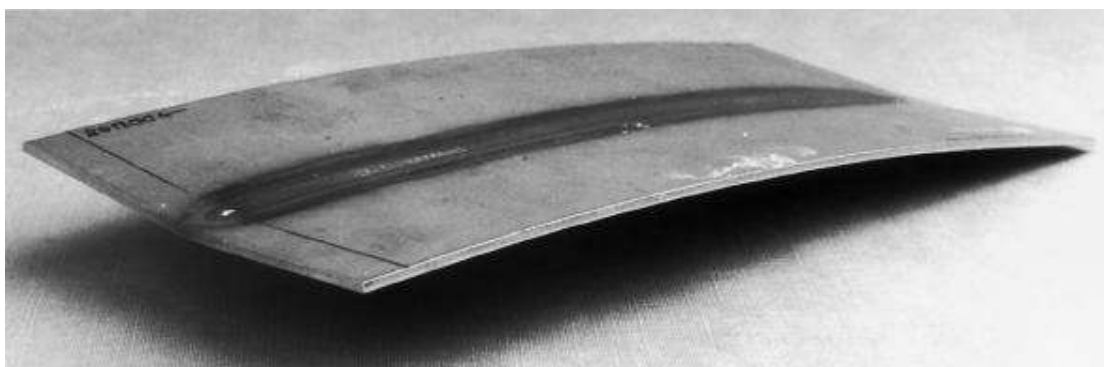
PLACA DE INCONEL 718 DE MEDIDAS 200 X 100 X 2 MM SOLDADA.
